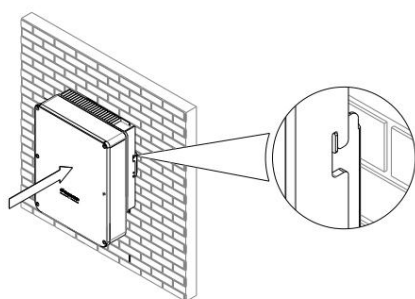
Pendure o inversor no suporte de montagem na parede
